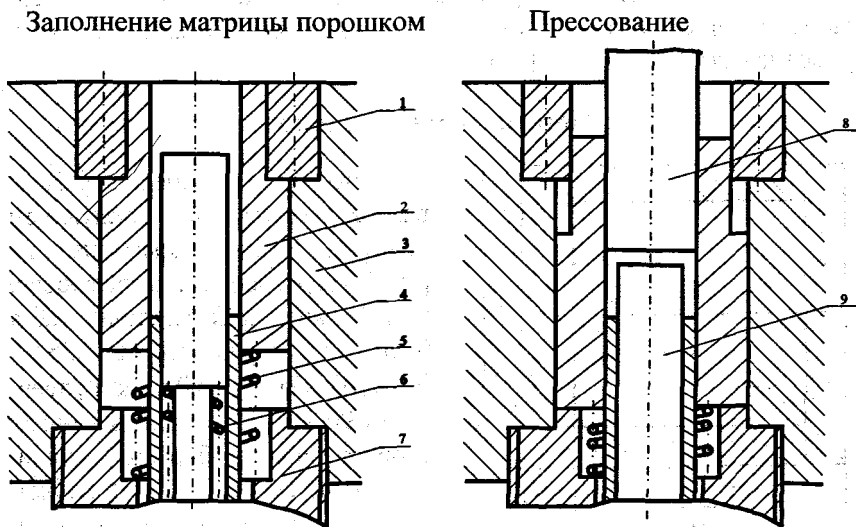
Схема прессования: 1 – кольцо; 2 – матрица; 3 – обойма; 4 – нижний пуансон; 5-6 – пружины; 7 – упор; 8 – верхний пуансон; 9 – стержень
